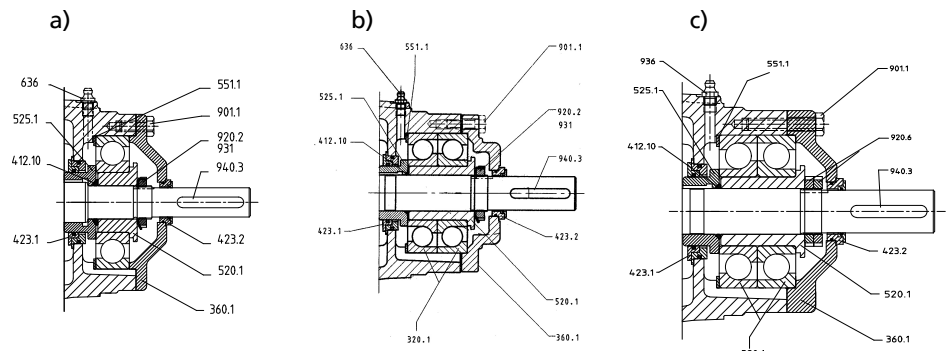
Консистентная смазка и лабиринтное уплотнение: а) типоразмер 32 и б) типоразмер 50-65 и с) типоразмер 100-150
